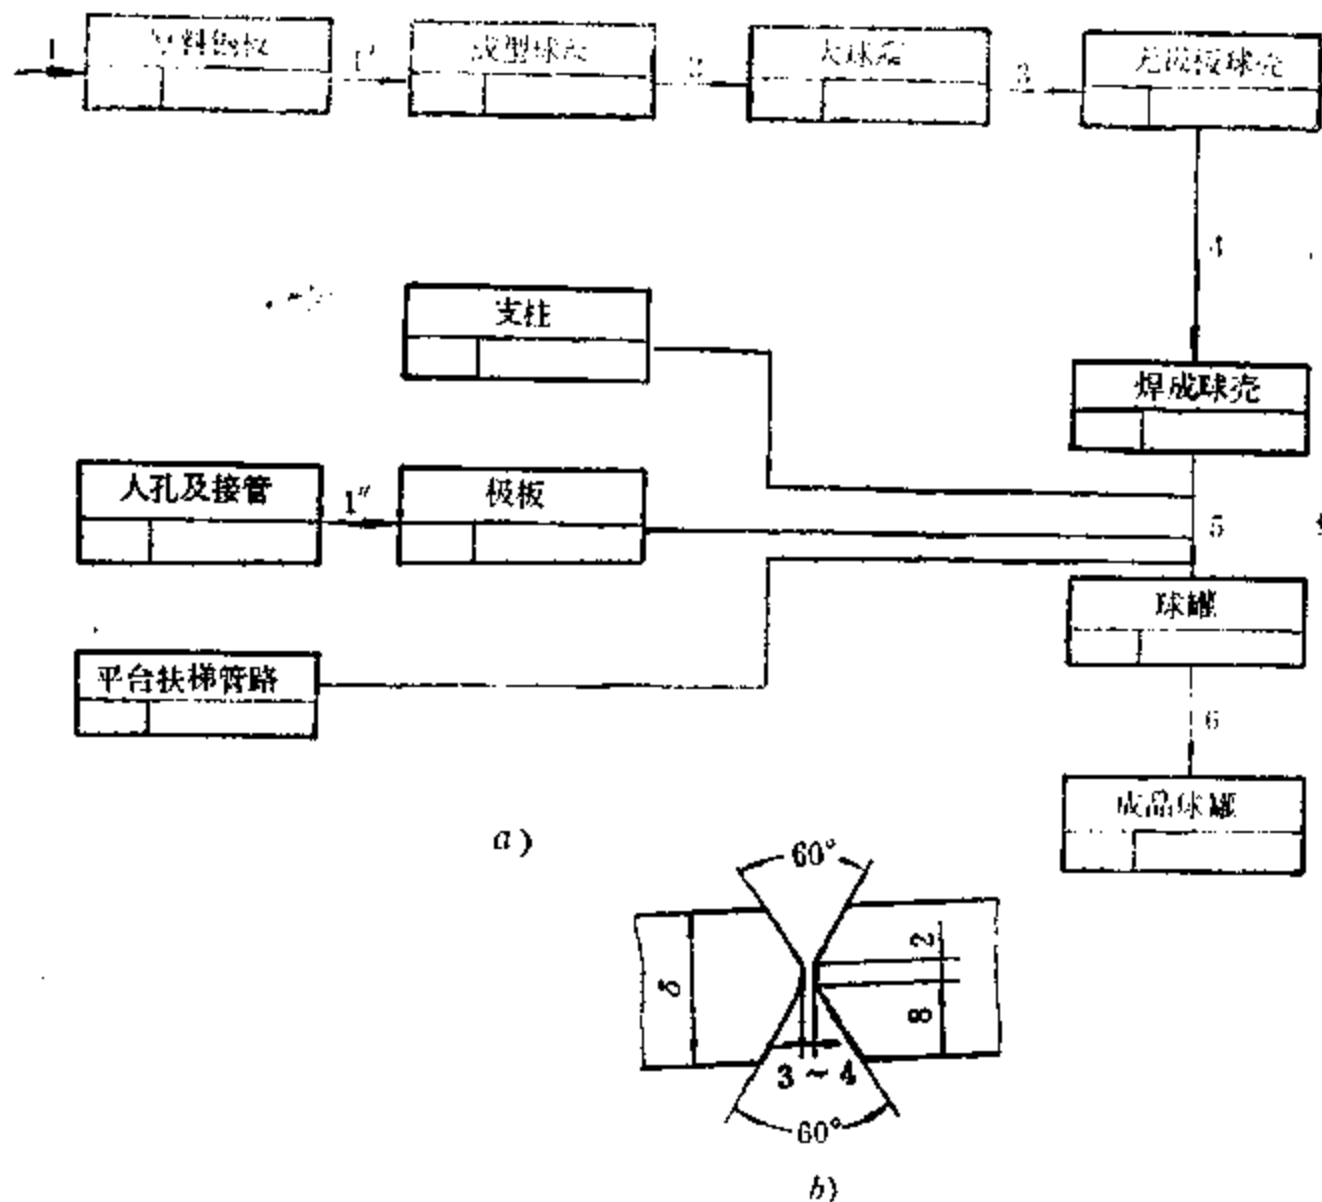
球罐焊接工艺路线 (a) 及焊缝坡口图 (b)
